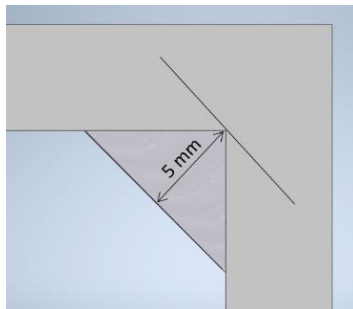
Tamaño de la garganta de la soldadura h .
